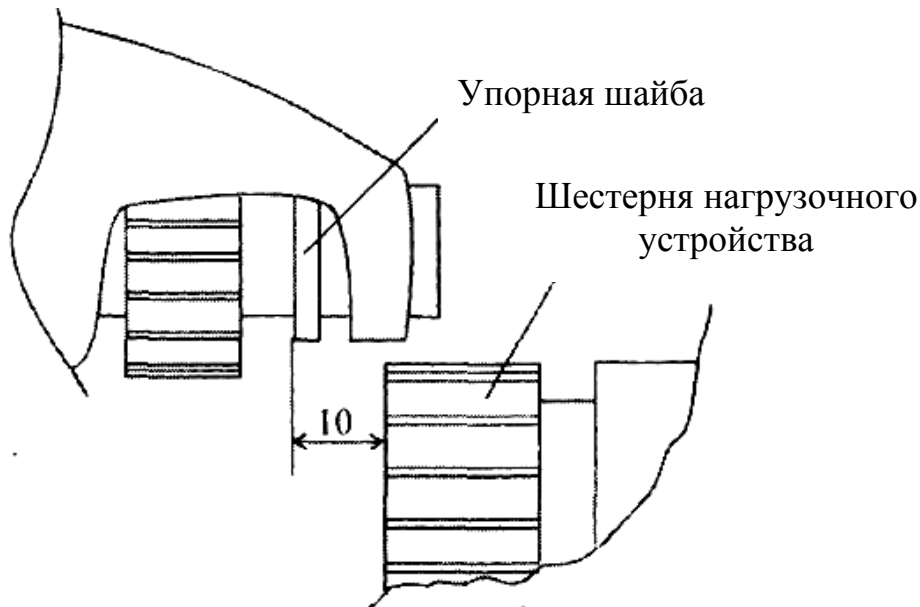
Взаимное расположение шестерни нагрузочного устройства стенда и упорной шайбы проверяемого стартера
